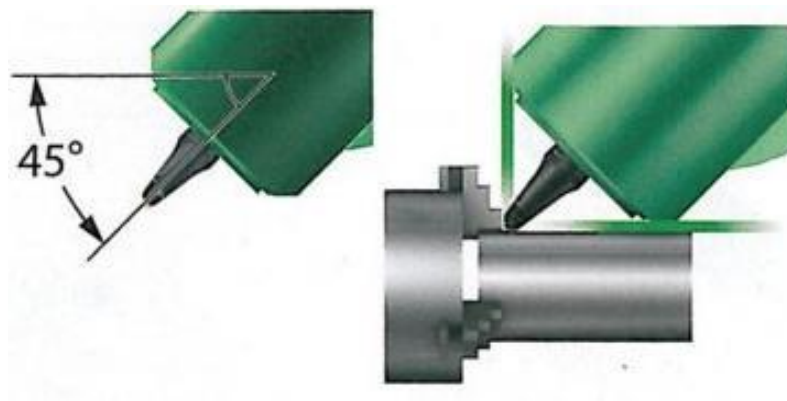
Положення фрезерного шпинделя під 45° .
